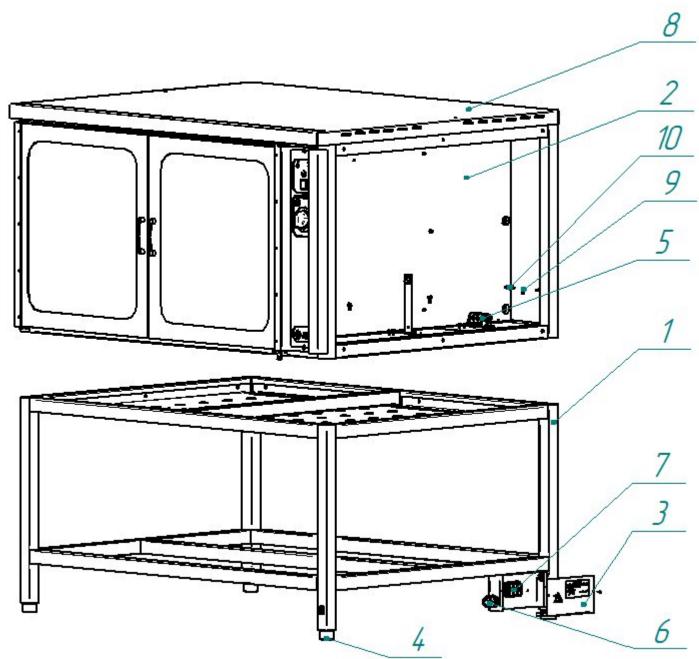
Схема сборки шкафа ШРТ 6-ЭШ-01
